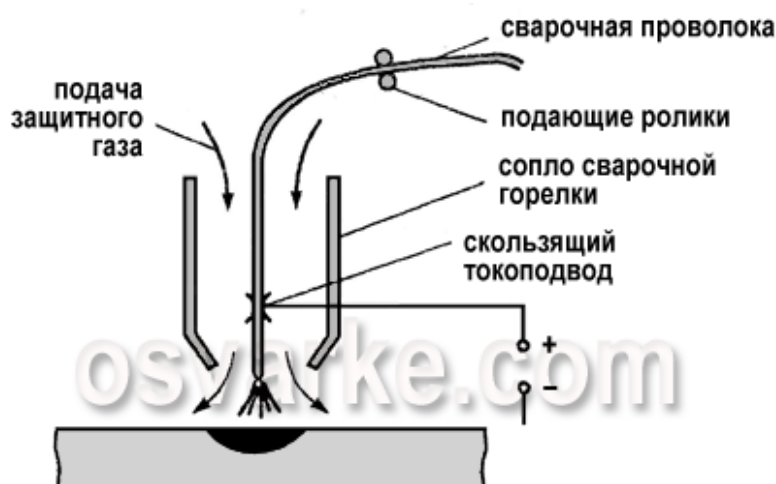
Схема сварки плавящимся электродом в защитных газах
